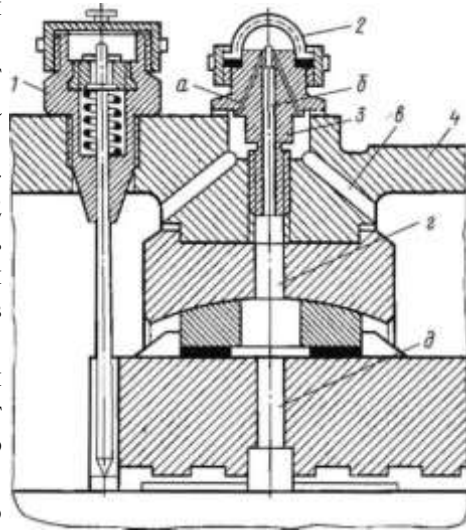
Устройство для контроля подачи масла к подшипникам
